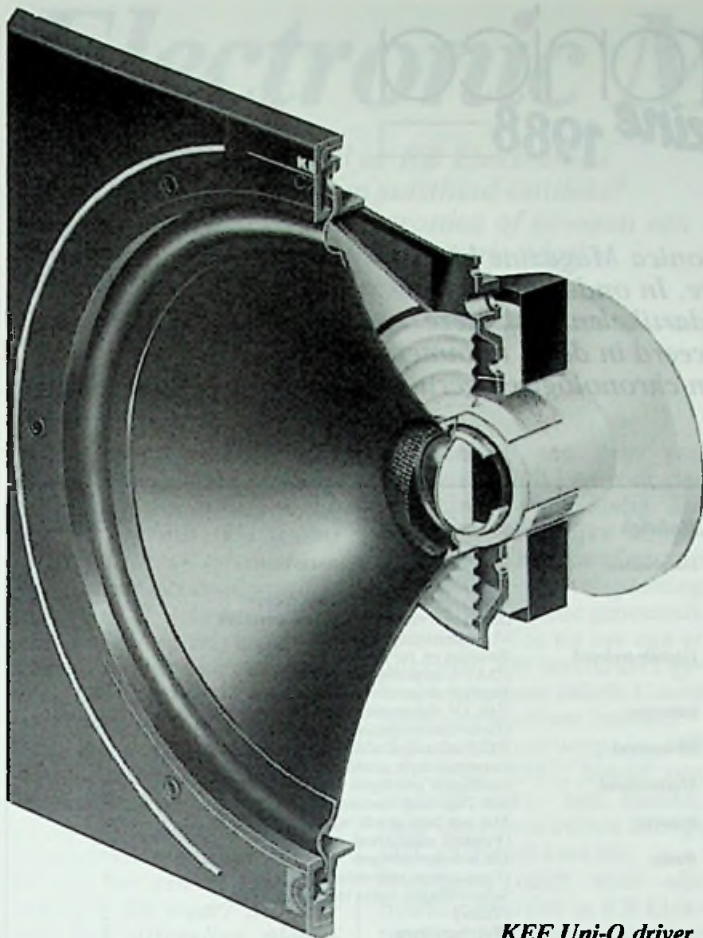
'Exploded view' van de KEF Uni-Q driver.
